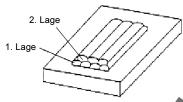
Prüfstück Form 1; 2-lagige-Auftrags
